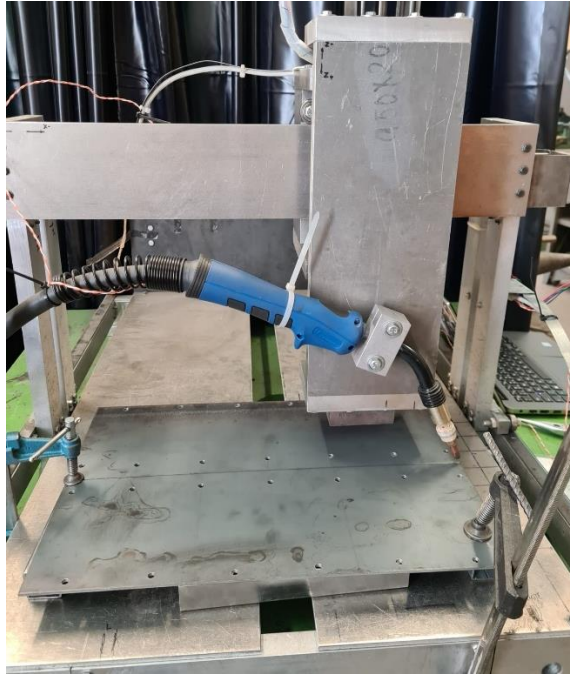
Chapas posicionadas no mecanismo de soldadura para execução dos cordões com ângulo de tocha em 25°.
